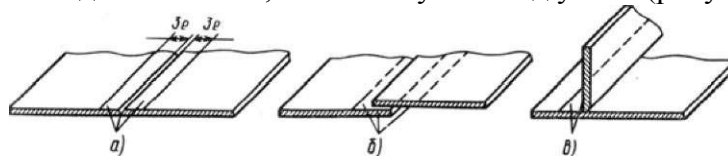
Подготовка кромок к пайке латунным припоем: а - участки, зачищенные до металла; б и в - зачистка до чистого металла
